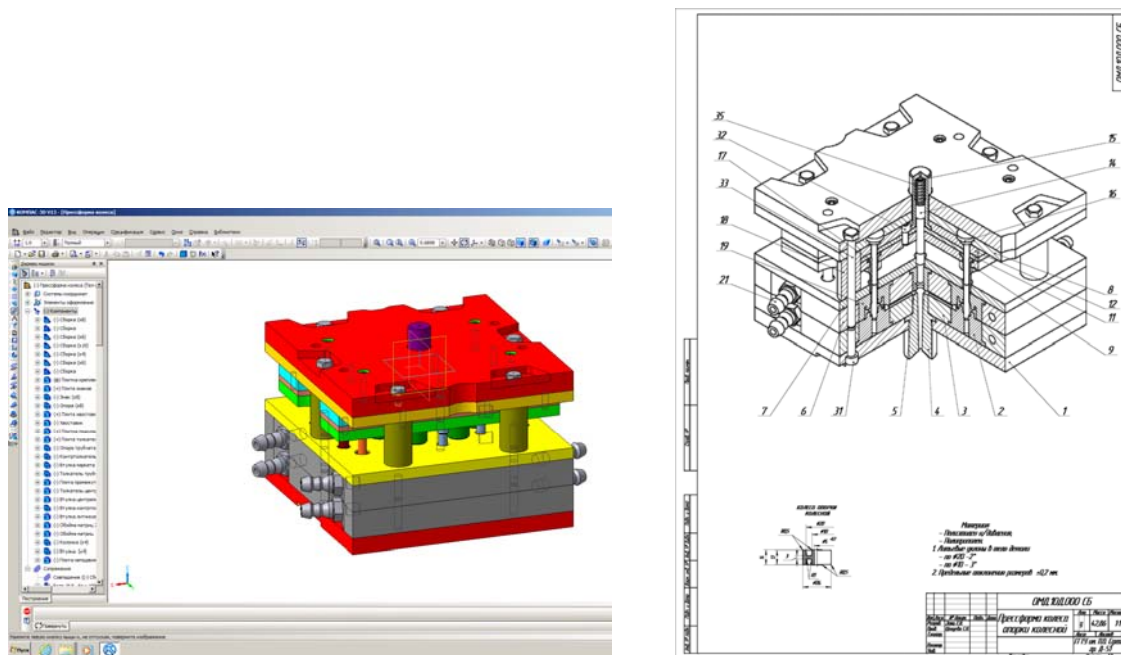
Сборочная 3D-модель и ассоциативный сборочный чертеж пресс-формы
